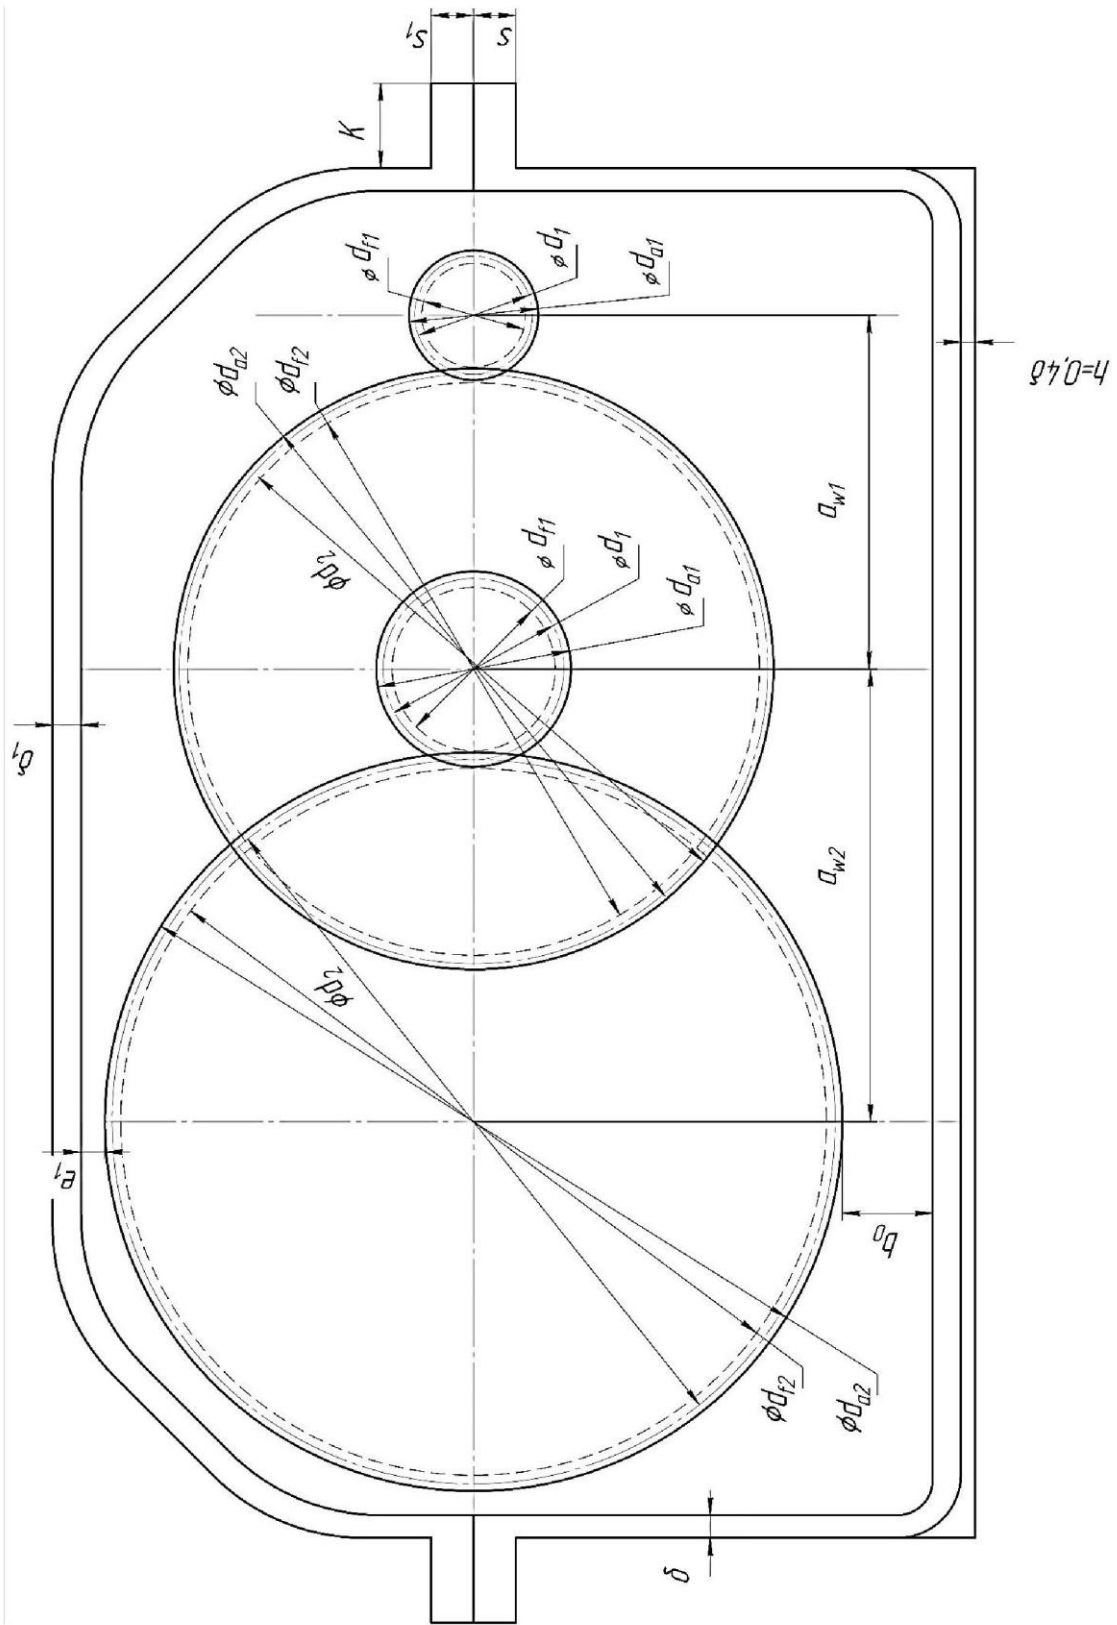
Компонувальне креслення двоступінчастого циліндричного редуктора (закінчення)
